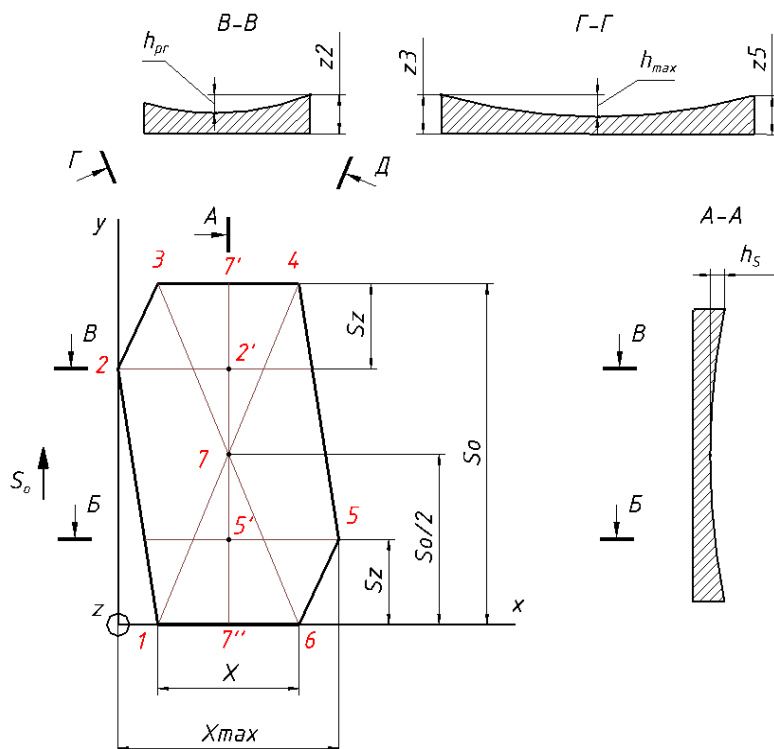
Общий вид ячейки, образованной за один оборот фрезой с круглым профилем режущей кромки
